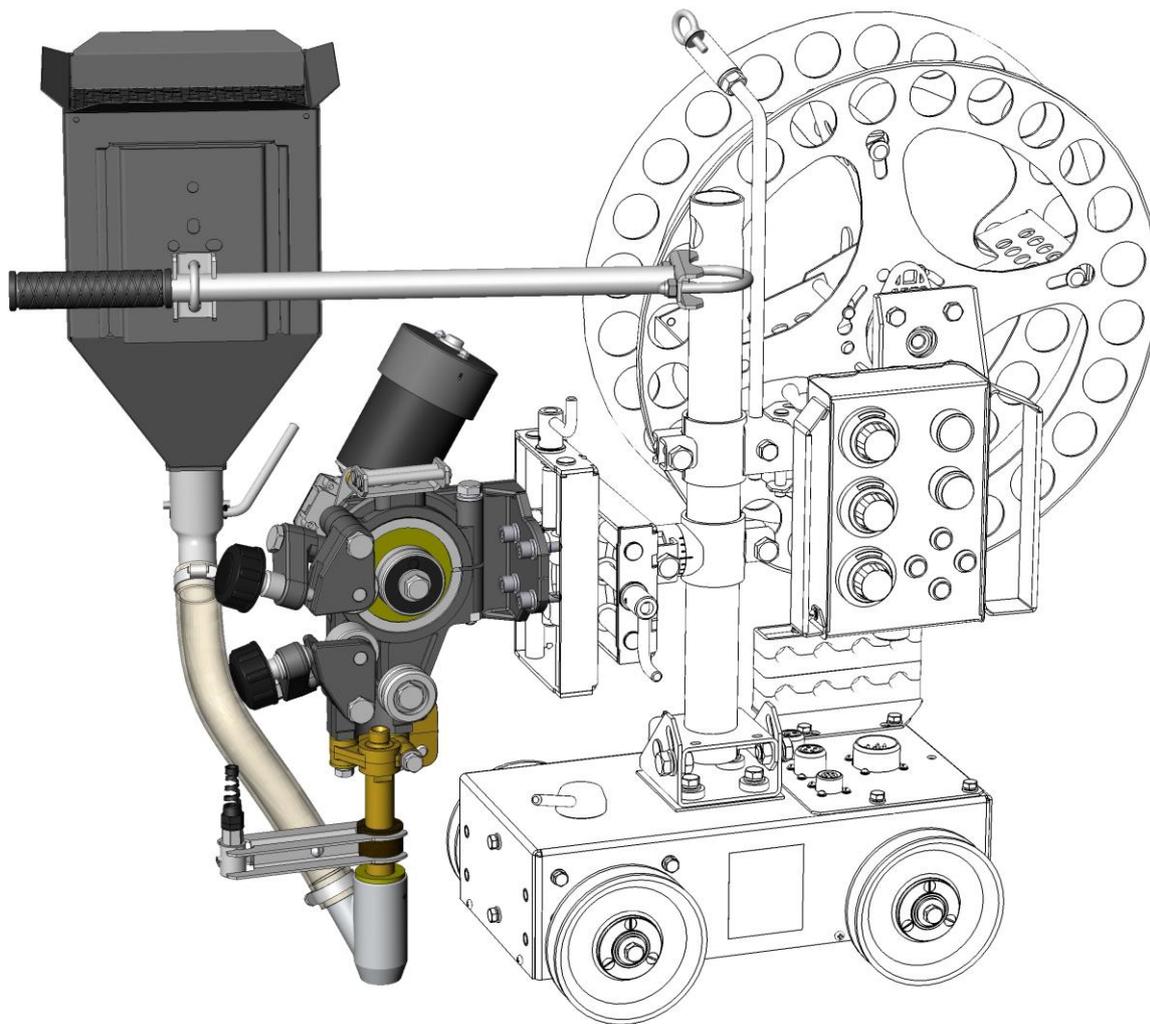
Комплект сварочной головки АДФ-1000 для сварки под флюсом проволокой $\varnothing 3,0-5,0$ мм.
